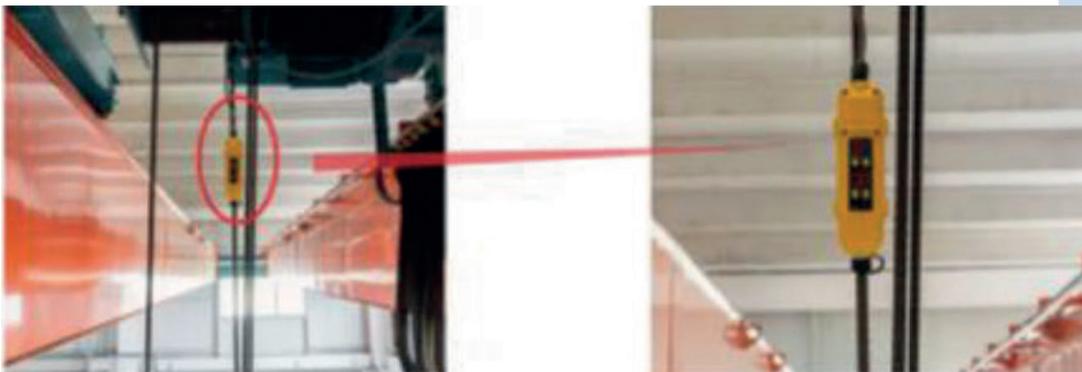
POSIÇÃO DE INSTALAÇÃO
